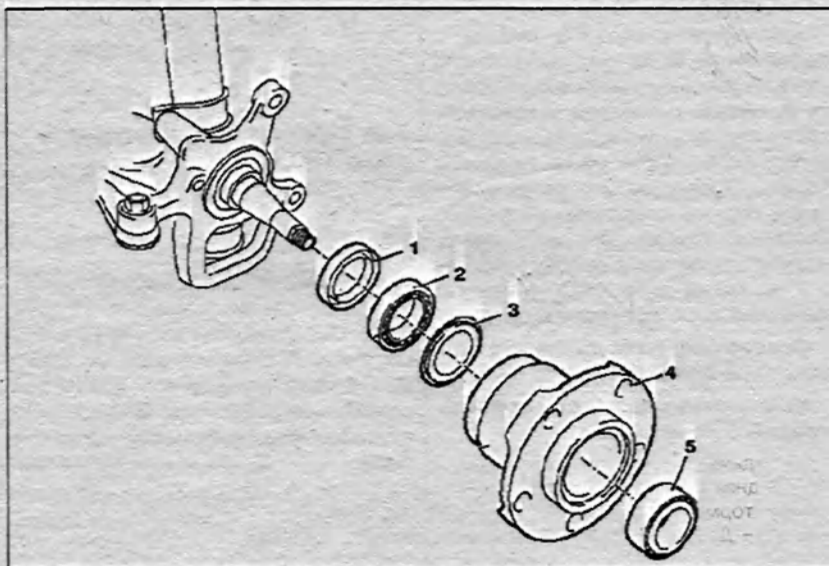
а. Разборка и сборка ступицы переднего колеса:
